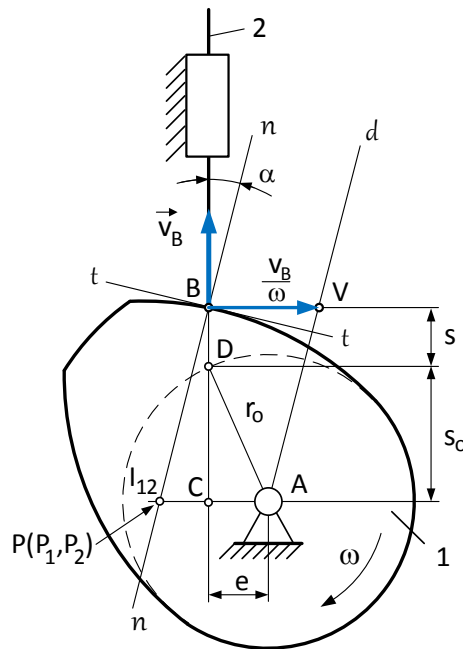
Legătura între unghiul de presiune și dimensiunile geometrice ale camei
